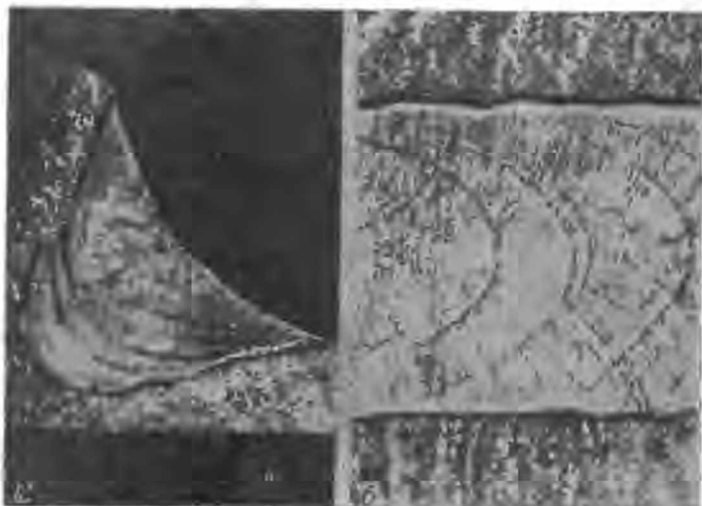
Столбчатость и слоистость строения сварного шва.
